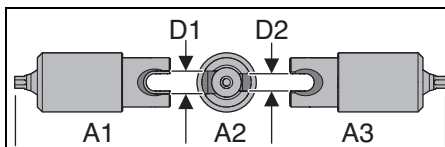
Vues de la pièce brute Ceramill Ti-Form
